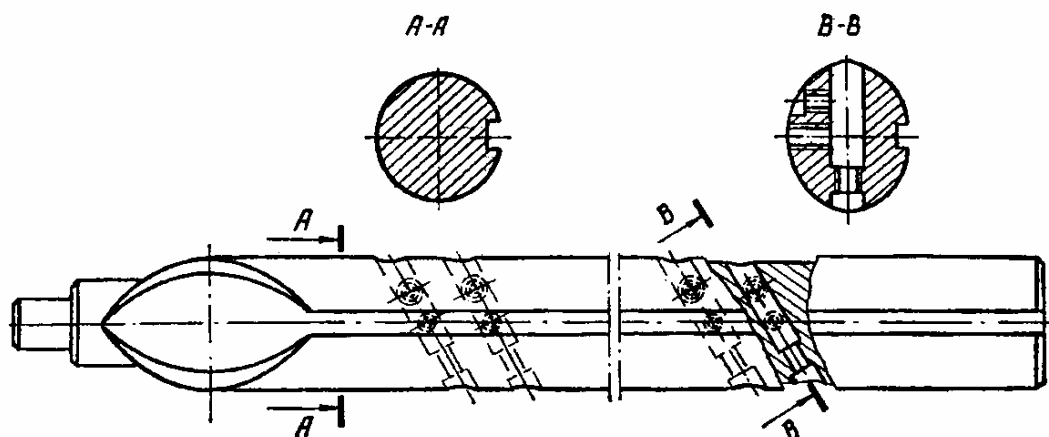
Борштанга для розточування гнізд корінних підшипників блока циліндрів
